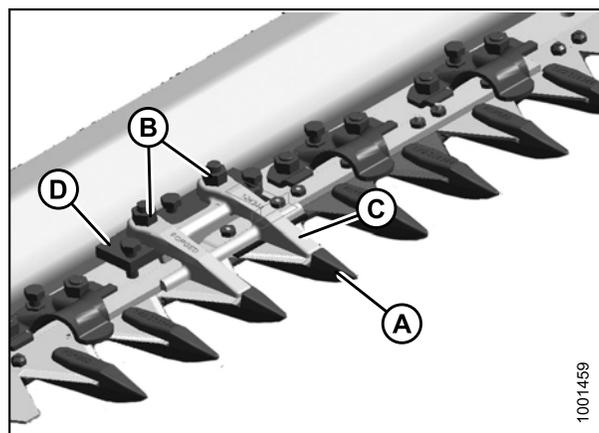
Противорежущий палец на жатке с двумя ножами
